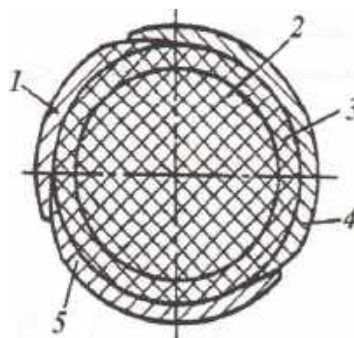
Схема розташування цулаг на поверхні заготовки:
